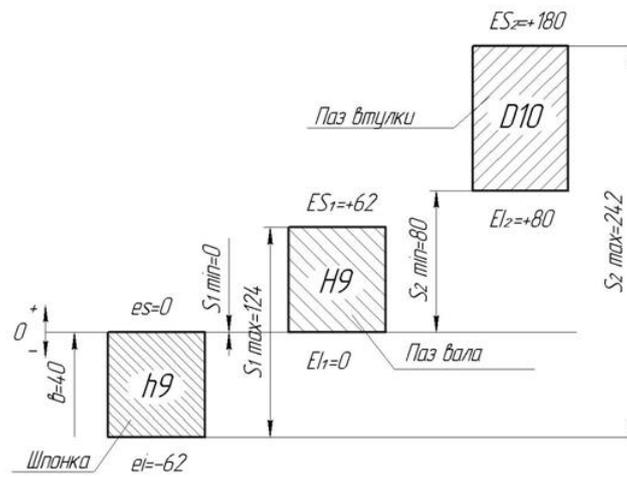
Схема розташування полів допусків вільного шпонкового з'єднання
